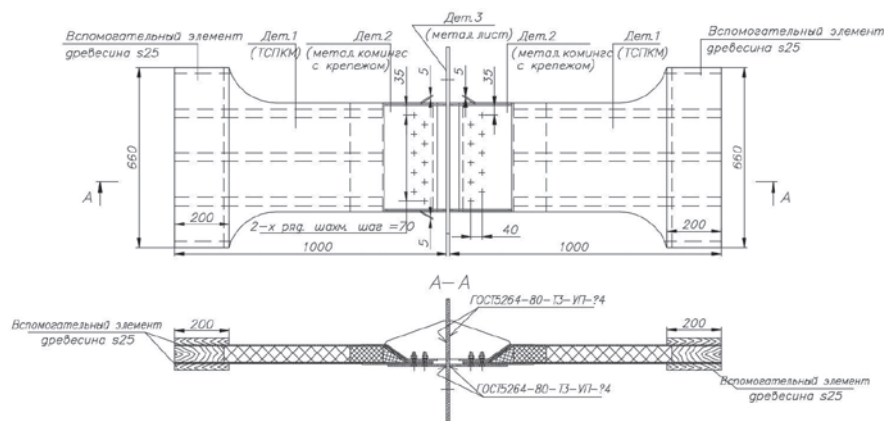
Чертеж макета узла соединения бортовой стенки надстройки из ТСПКМ с металлическим корпусом корабля для проведения испытаний
